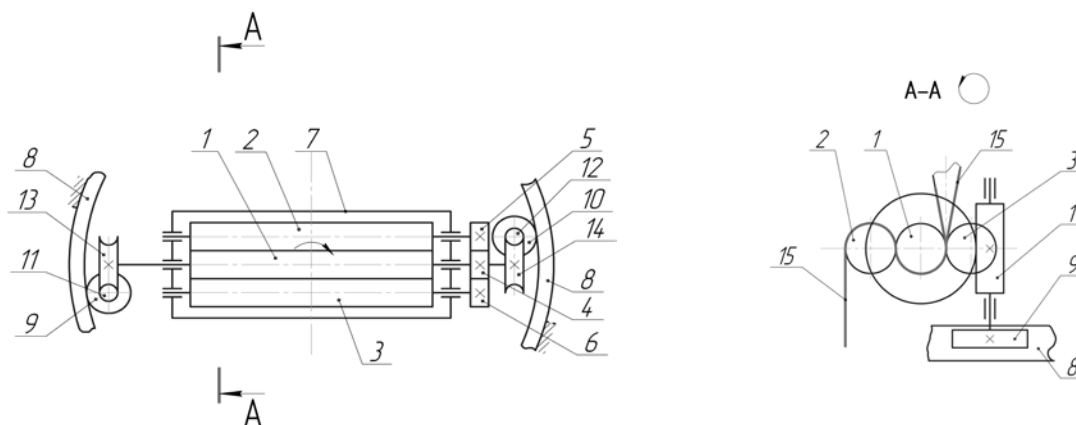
Кінематична схема механізму відтягнення полотна круглов'язальної машини: 1 – ведучий відтяжний валик; 2, 3 – ведені відтяжні валики; 4, 5, 6 – циліндричні шестерні; 7 – рама; 8 – зубчасте колесо; 9, 10 – шестерні; 11, 12 – черв'яки; 13, 14 – черв'ячні колеса; 15 – полотно
